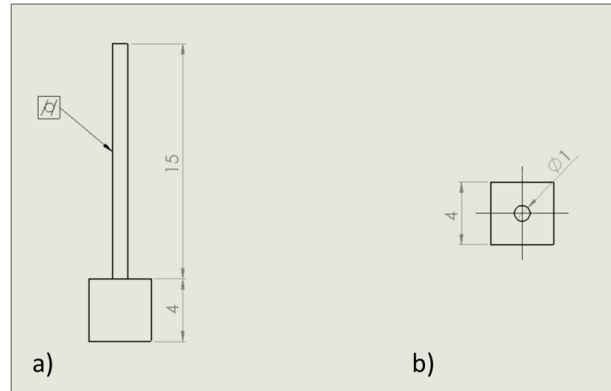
Dessin technique du cylindre, avec mesure de cylindricité a) vu de côté ; b) vu du dessus, en mm
